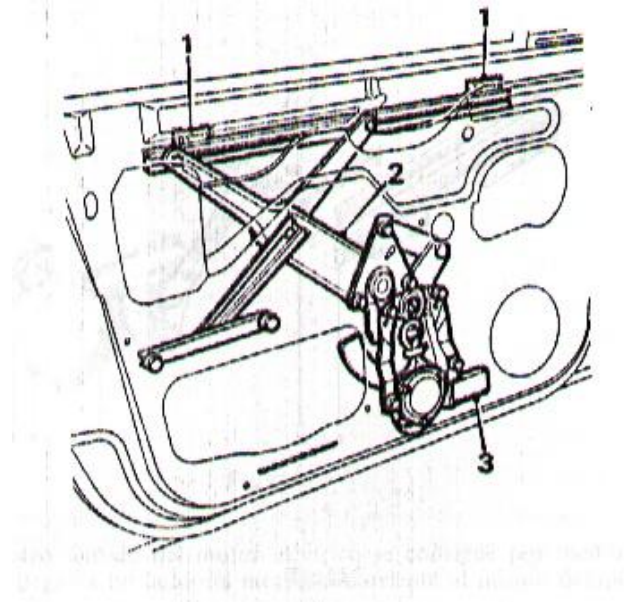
CONJUNTO DE ELEMENTOS DEL MECANISMO DE ELEVAVIDRIOS
